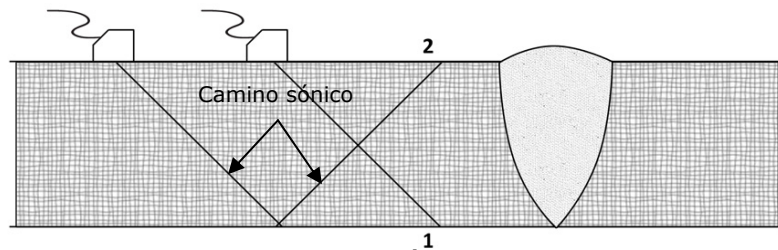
Recorrido del eco ultrasónico desde la salida del transductor hasta la base y alto del refuerzo de la soldadura.
